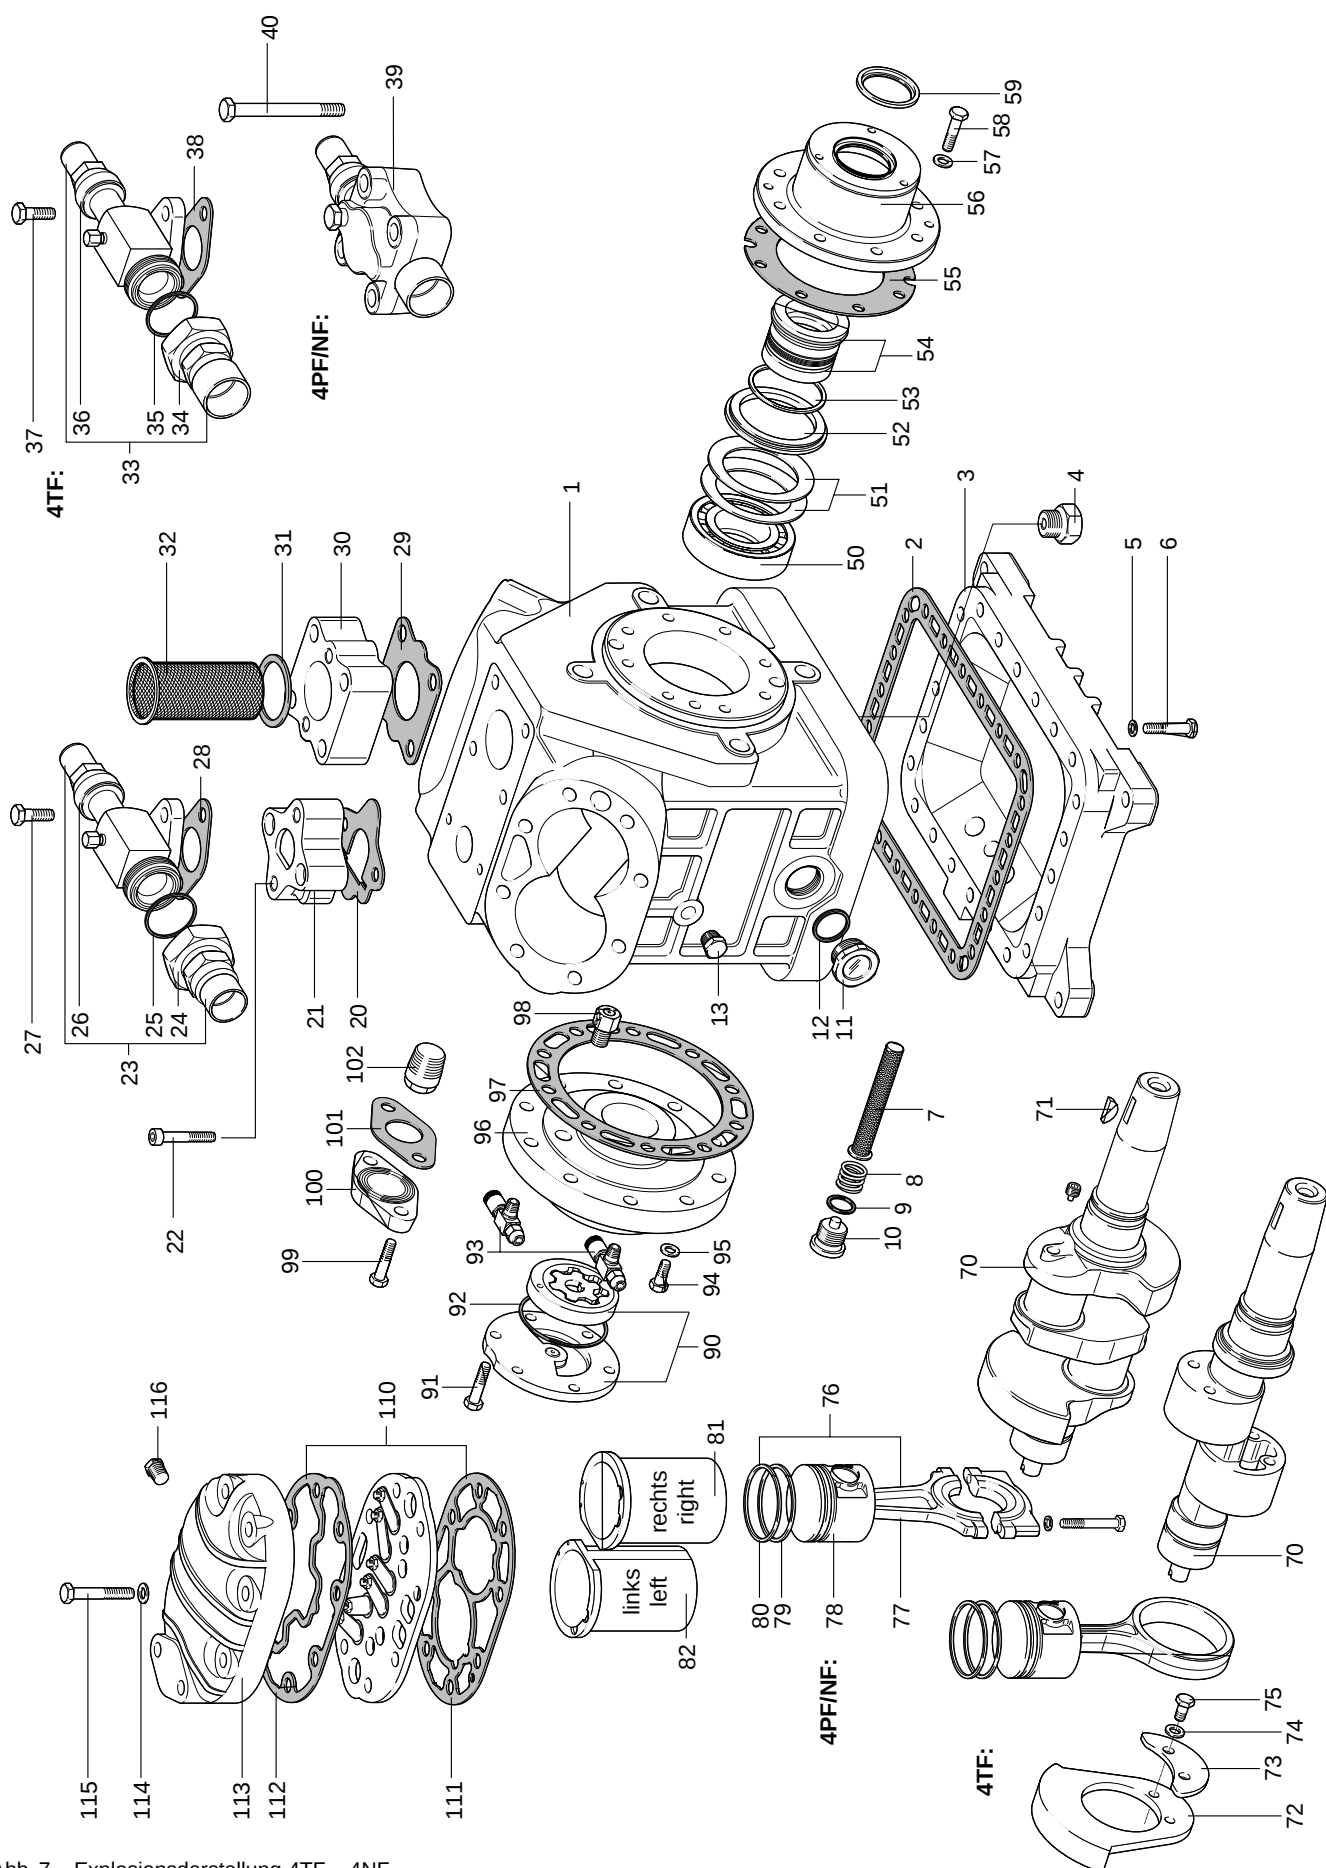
Explosionsdarstellung 4TF .. 4NF
